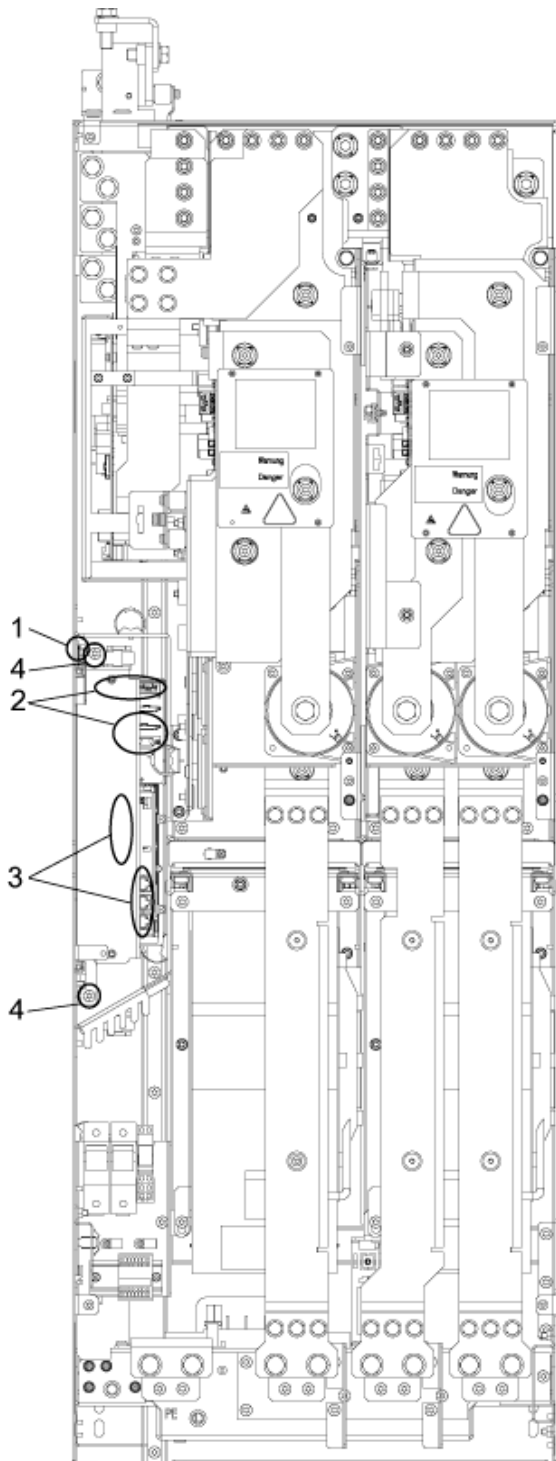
Austausch Control Interface Board, Baugröße HX
